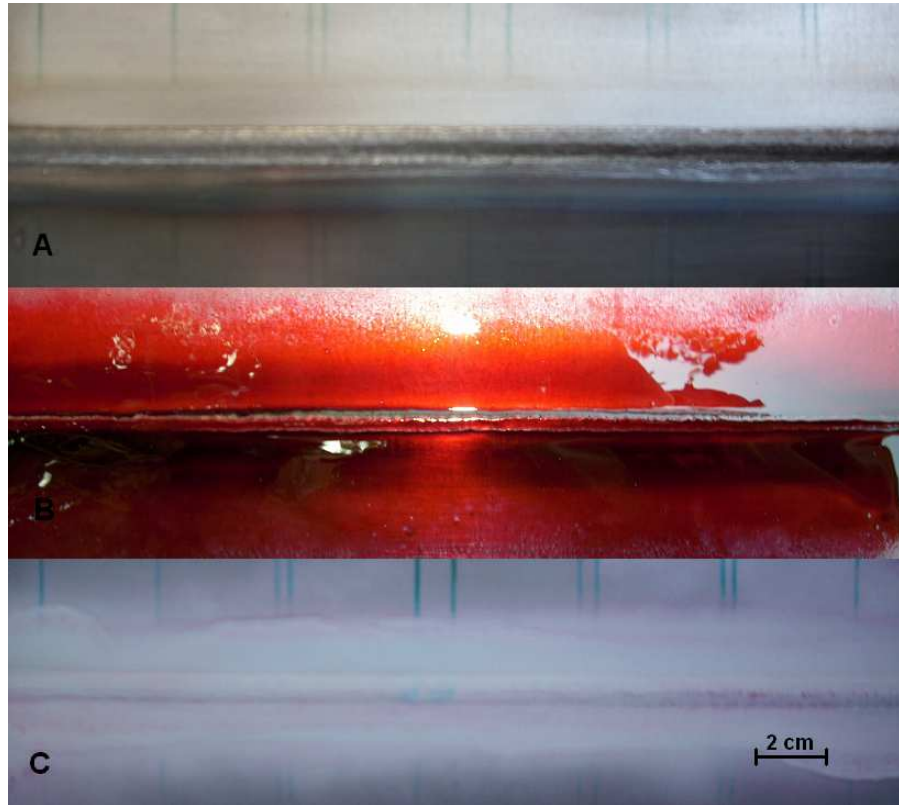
A.- Limpieza con Removedor del cupón soldado. B.- aplicación del Penetrante sobre el cupón soldado. C.- Aplicación del Revelador sobre el cupón soldado. (Lado del refuerzo de Cara).
